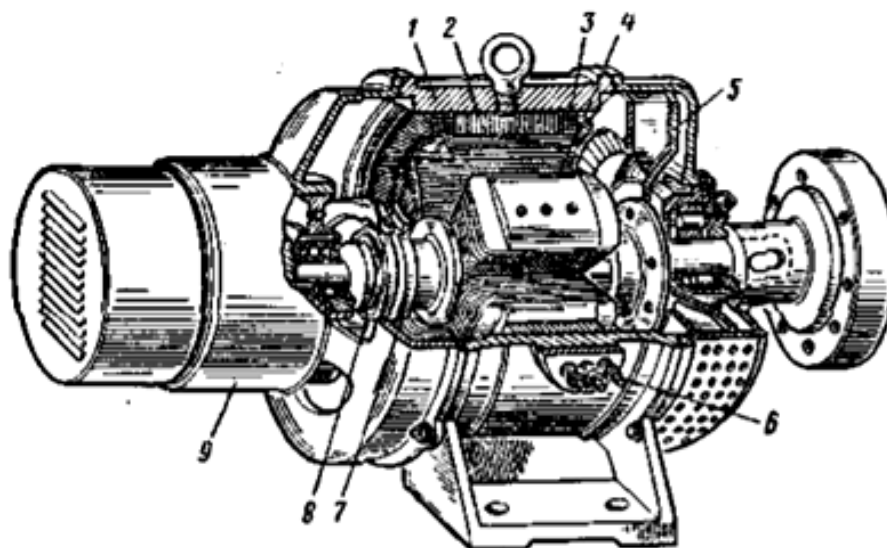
Устройство явнополюсной машины: 1 – корпус; 2 – сердечник статора; 3 – обмотка статора; 4 – ротор; 5 – вентилятор; 6 – выводы обмоток; 7 – контактные кольца; 8 – щетки; 9 – возбудитель
